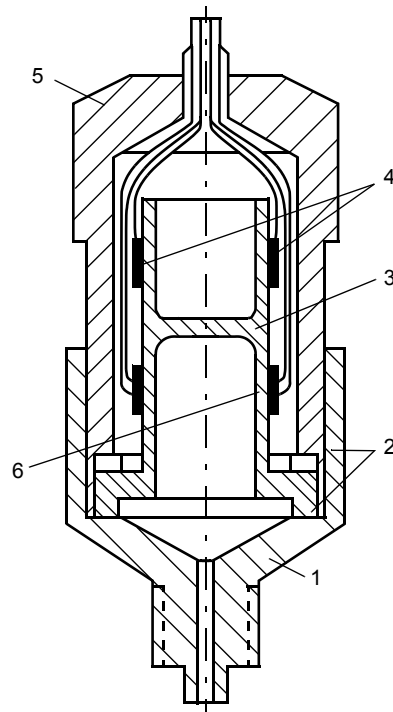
Конструкция тензометрического датчика: 1 — штуцер; 2 — прокладки; 3 — датчик-втулка; 4 — пассивный проволоочный тензодатчик; 5 — гайка; 6 — основные датчики
